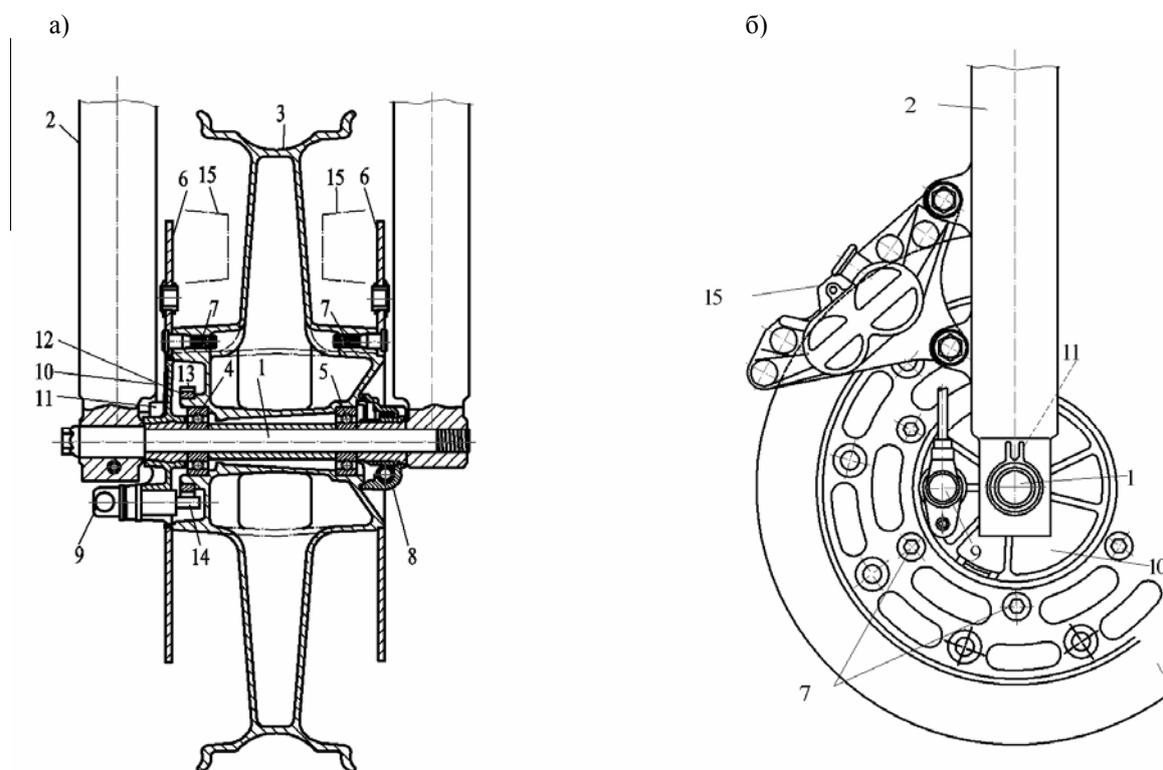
Дисковый тормозной механизм с элементами антиблокировочной системы: а – разрез дискового тормозного механизма; б – вид сбоку дискового тормозного механизма; 1 – ось; 2 – передняя вилка; 3 – переднее колесо; 4 – подшипник; 5 – подшипник; 6 – диск тормозной; 7 – болт; 8 – датчик скорости спидометра; 9 – датчик скорости колеса; 10 – пластина датчика скорости колеса; 11 – стопор; 12 – кольцо датчика скорости колеса; 13 – шестернеподобные профили кольца датчика скорости; 14 – чувствительный элемент; 15 – дисковый тормоз
